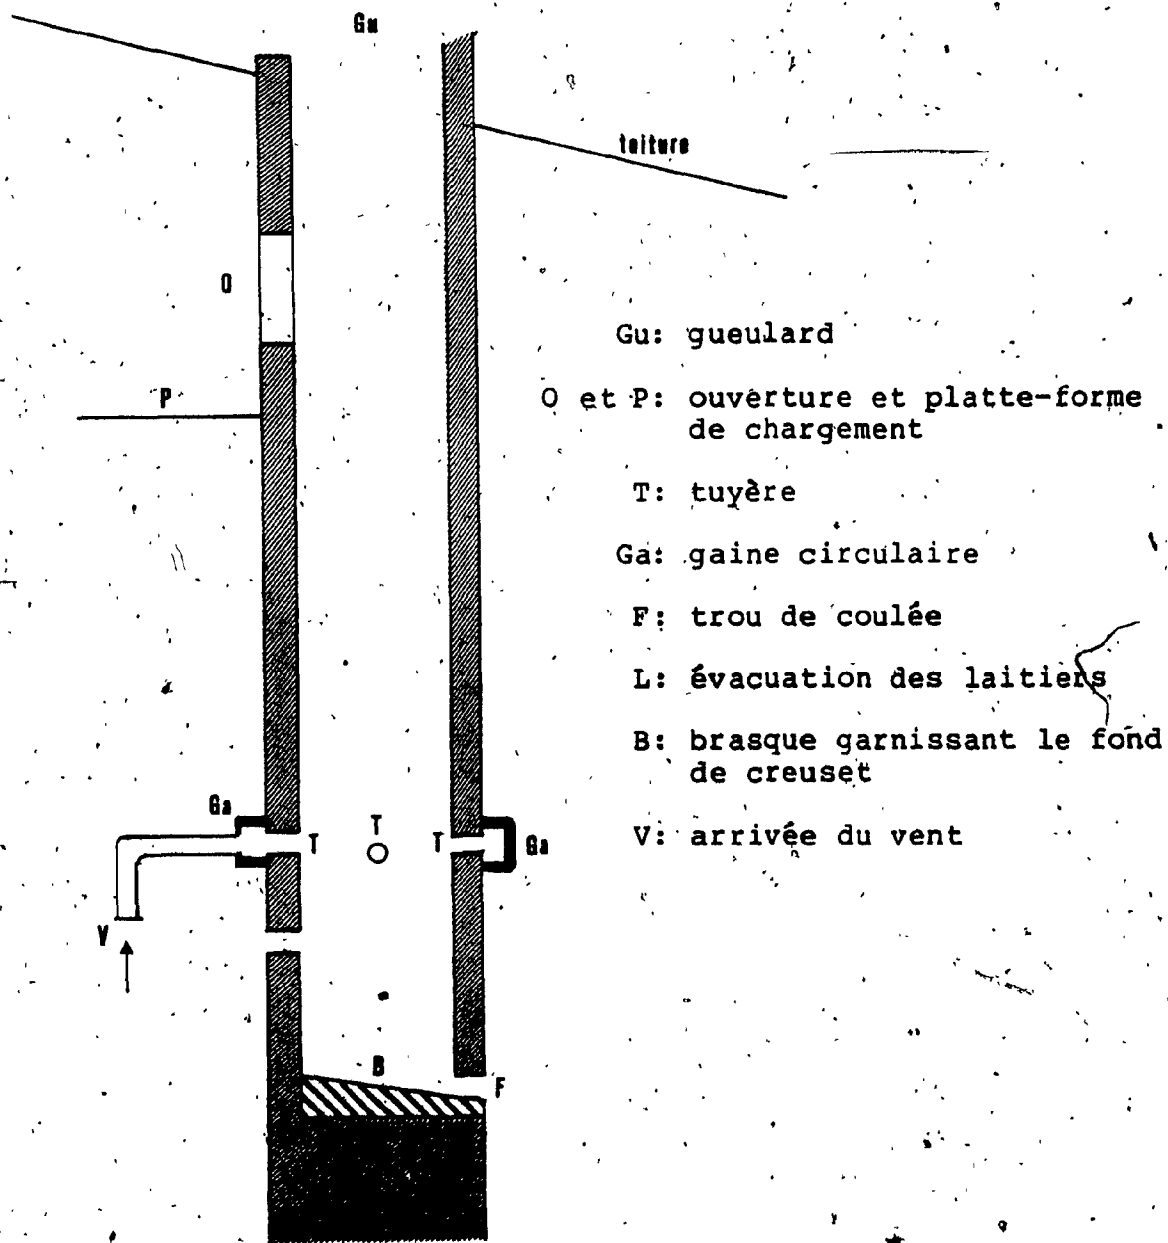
Coupe longitudinale d'un cubilot à vent soufflé.
